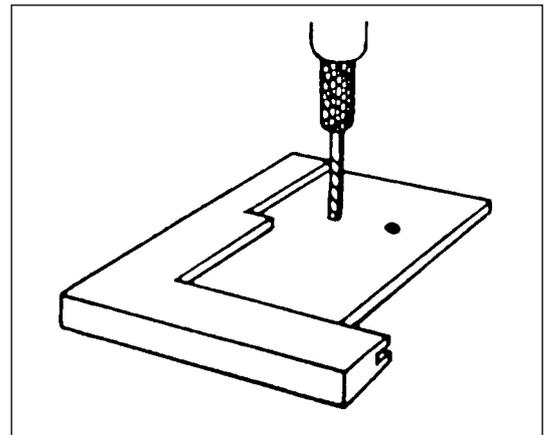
Utiliser un dispositif de serrage ou de fixation spécialement adapté ou universel au lieu de maintenir à la main une pièce travaillée instable
